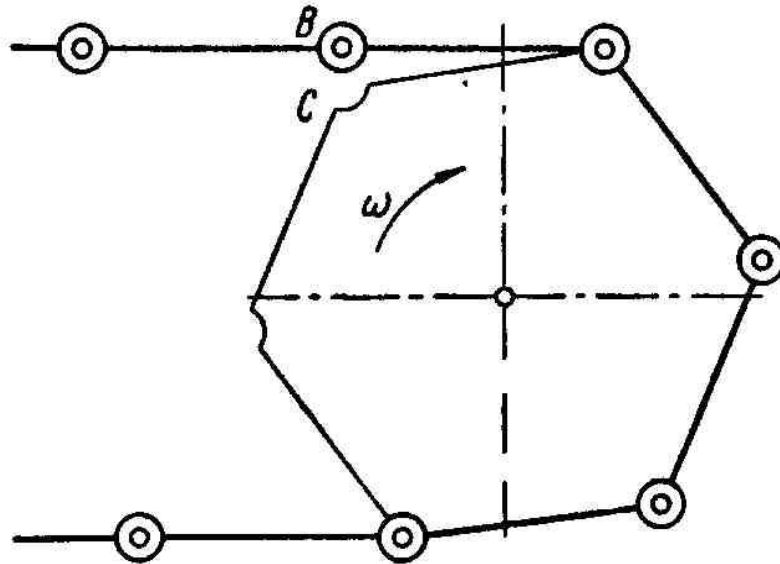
Схема расположения цепи в момент вхождения шарнира в зацепление с зубом звездочки
